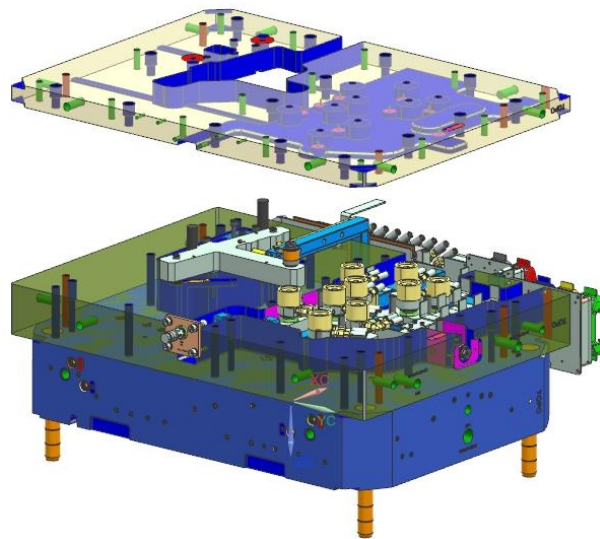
Montagem da placa de alojamento do sistema de injeção
